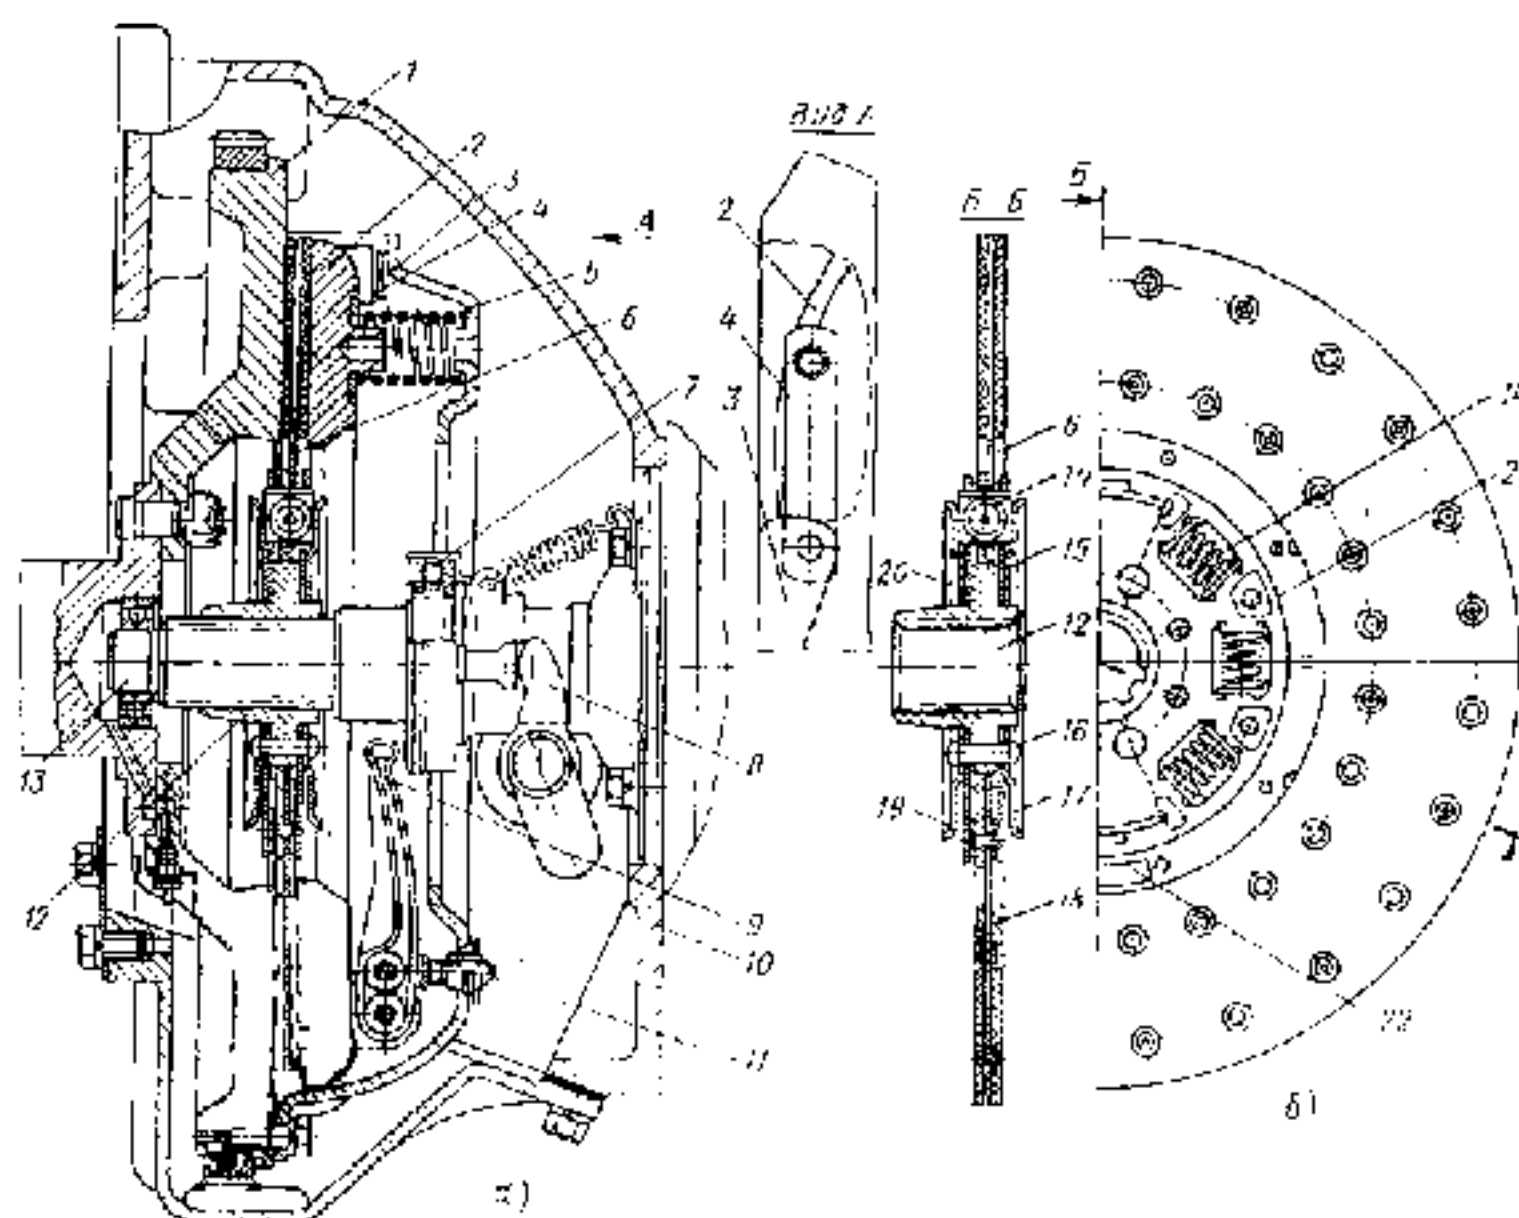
Сцепление автомобиля ЗИЛ-130: а – общий вид; б – ведомый диск.
